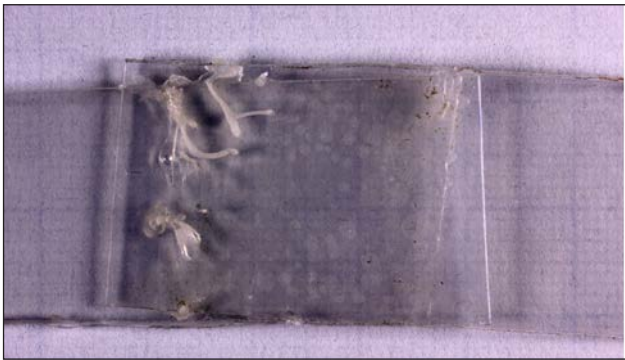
Ультразвуковий напускний зварний шов біорозкладної плівки, виконаний сонотродом із рівною поверхнею
